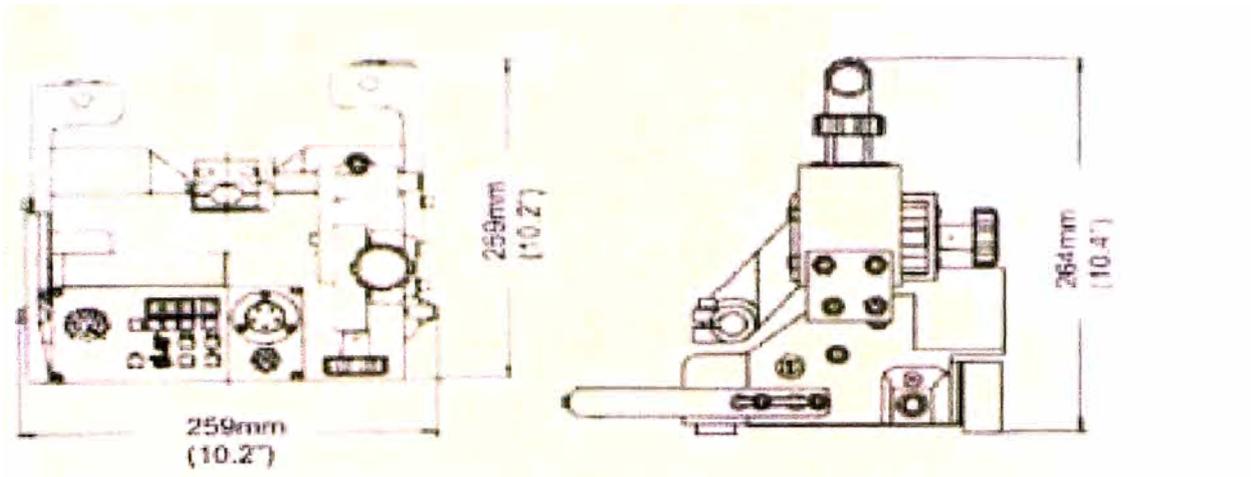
Dimensiones de Equipo de Corte WEL-HANDY MULTI, Marca: KOIKE
